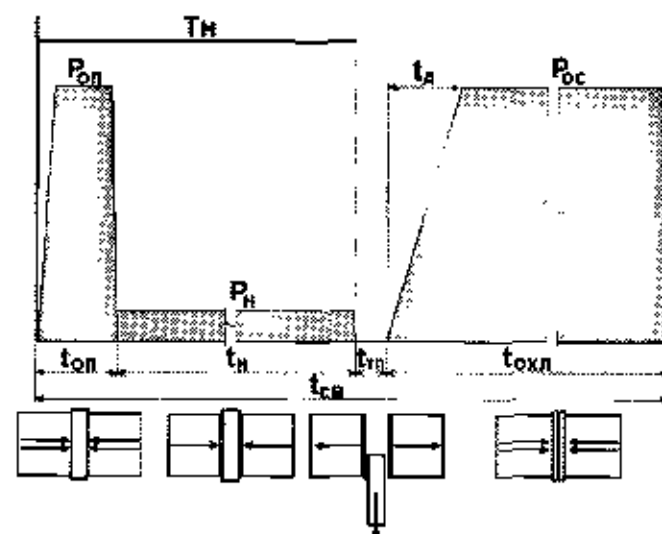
Циклограмма процесса стыковой сварки
